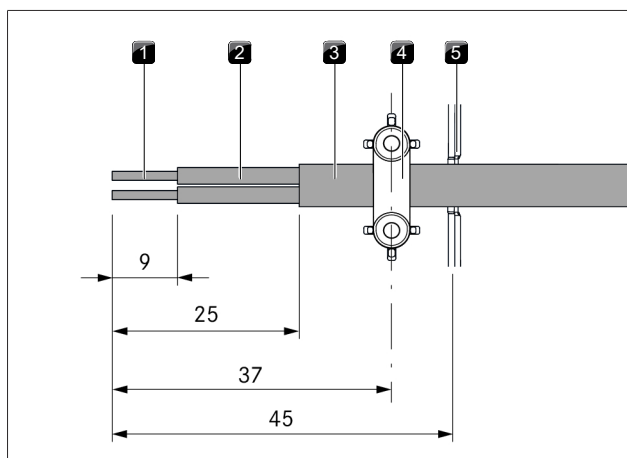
Comprimentos de decapagem e posição de montagem do cabo de ligação
